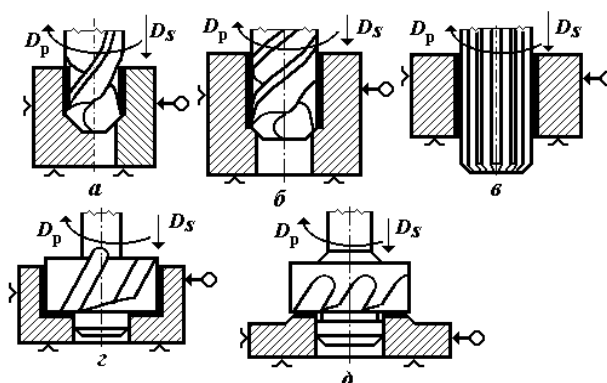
Основные технологические схемы сверления: а – сверление и рассверливание; б – зенкерование; в – развертывание; г - зенкование; д – цекование
